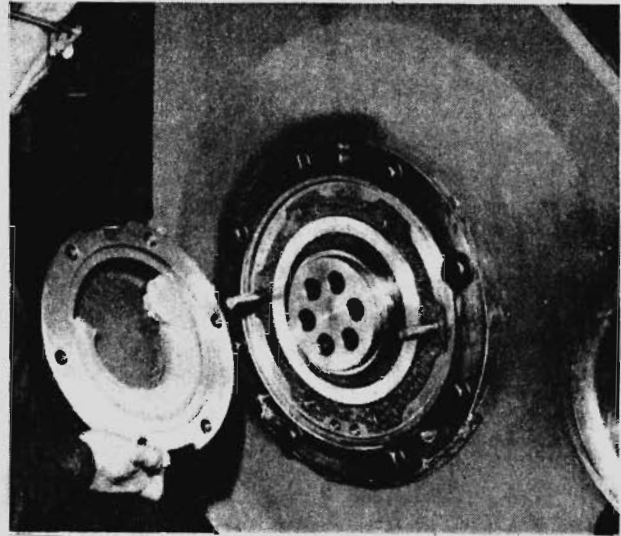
Montando una cubierta de cojinete de extremo de colector
